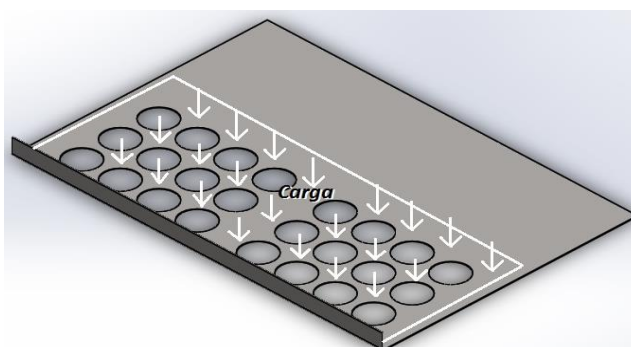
Distribución de la carga en la sección 2 de la placa
